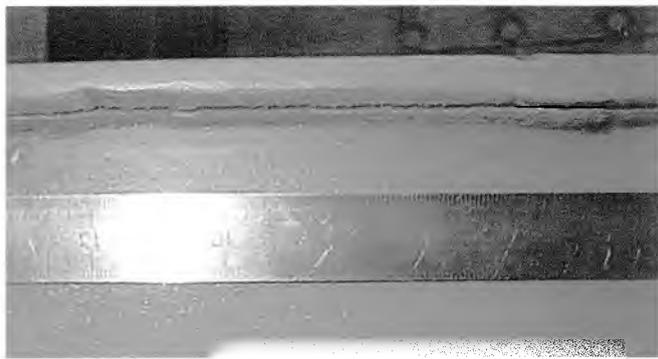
Продольная трещина таврового сварного соединения коробчатой конструкции подъемного сооружения на фоне поверхности с лакокрасочным покрытием
